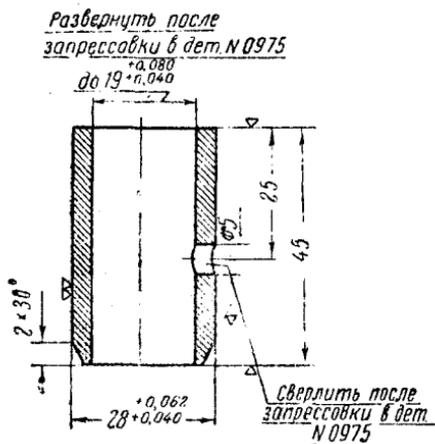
Дет. № 0976. Втулка корпуса валика масляного насоса
